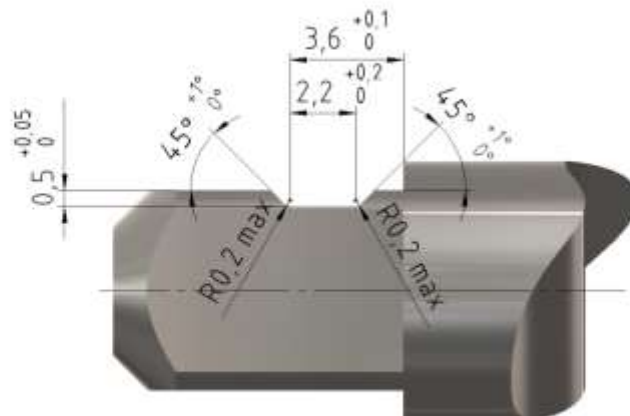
Maße der Nut für Gewindewerkzeuge mit Schaftdurchmesser 3,5 – 11,2 mm (Form A)
